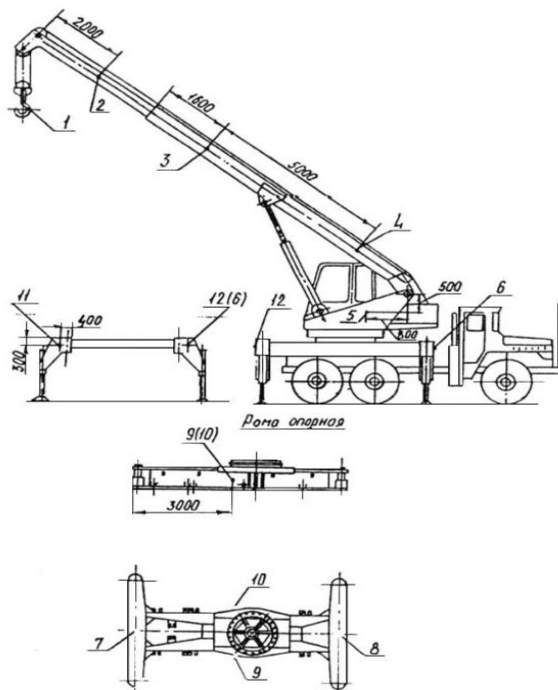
Рекомендуемая схема расположения ПАЭ для АЭ-контроля металлоконструкций кранов.
